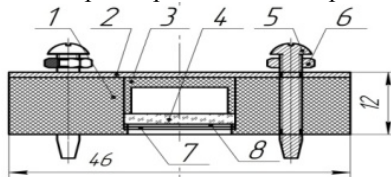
Конструкция фантома: 1 – корпус; 2 – крышка; 3 – прижимной стакан; 4 – флуоресцирующий образец; 5 – винт-ножка; 6 – фиксирующая гайка; 7 – проставочное кольцо; 8 – рассеивающий элемент
